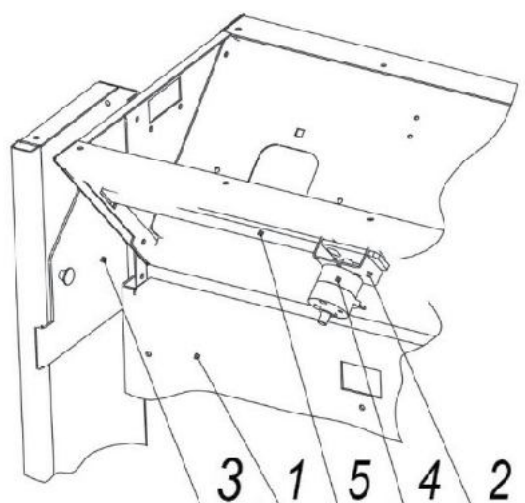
Установка блокировочных замков привода заземляющего разъединителя
